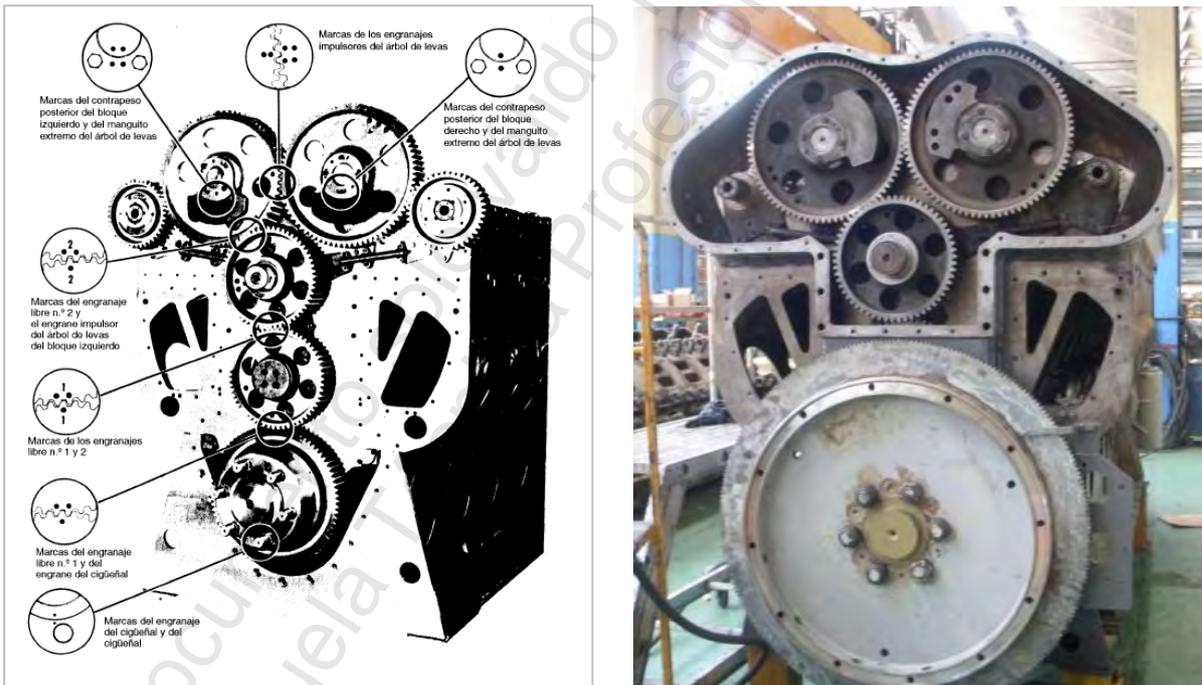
Engranajes que integran la cadena de distribución en motor de dos tiempos GM 16- 645C
